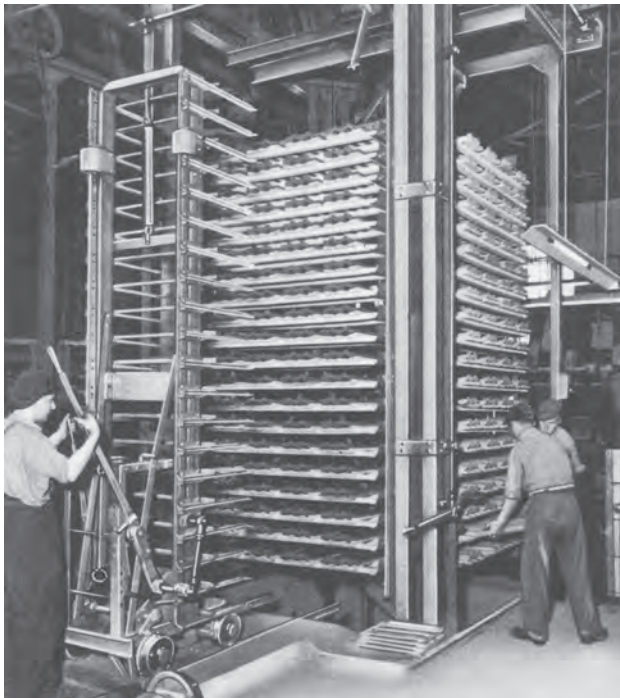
4-seitiges Hub- und Senkgerüst in einem Dachziegelwerk, um 1960
